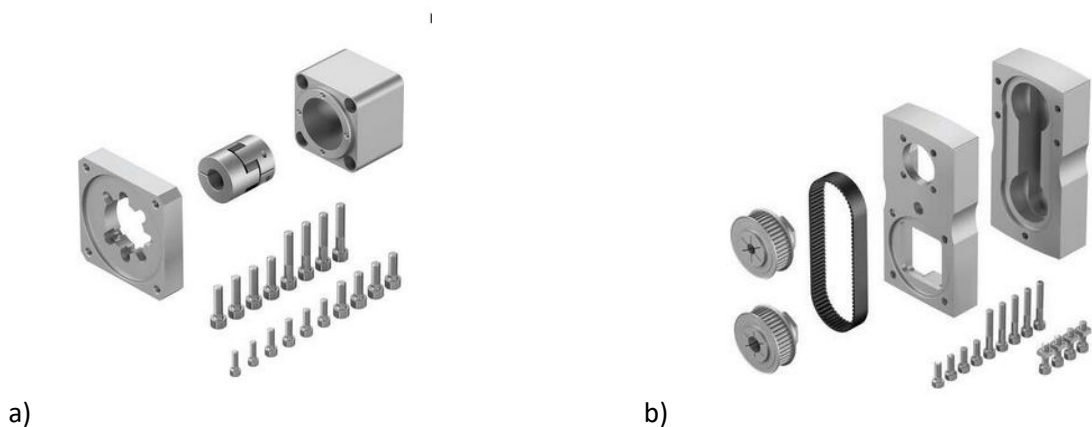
a) Vue éclatée du kit axial simple ; b) Vue éclatée du kit axial parallèle
